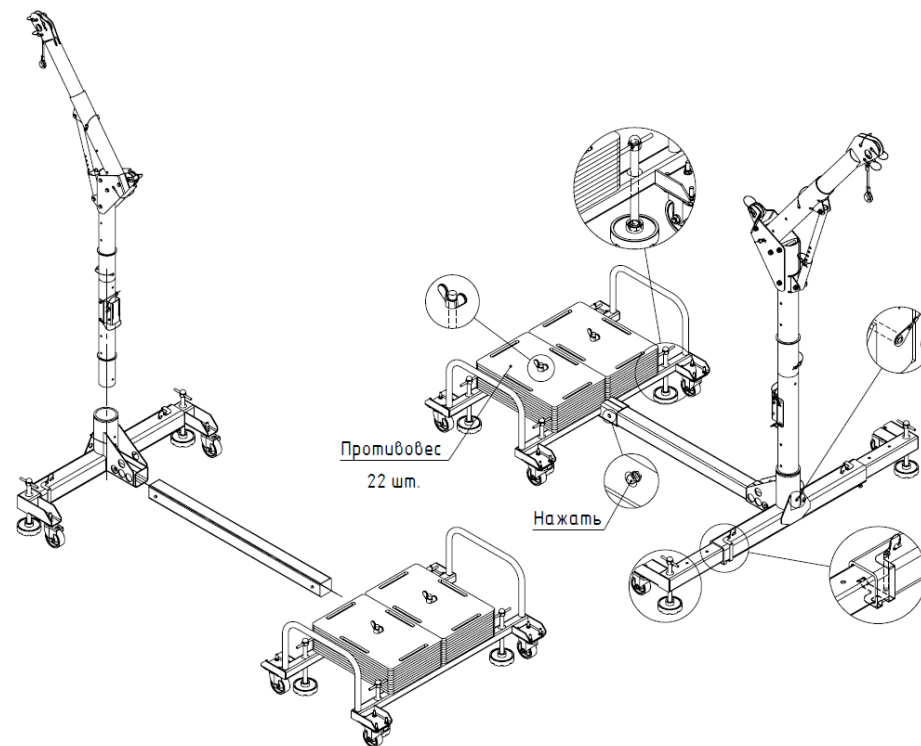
Монтаж СОБ Кран Е11-4Н
